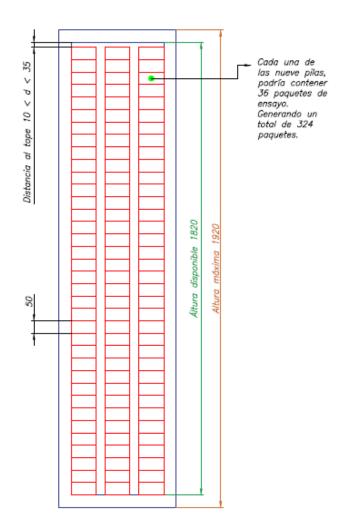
4 Paquetes ubicados en elevación en la sección congeladora. Fuente Autores.
